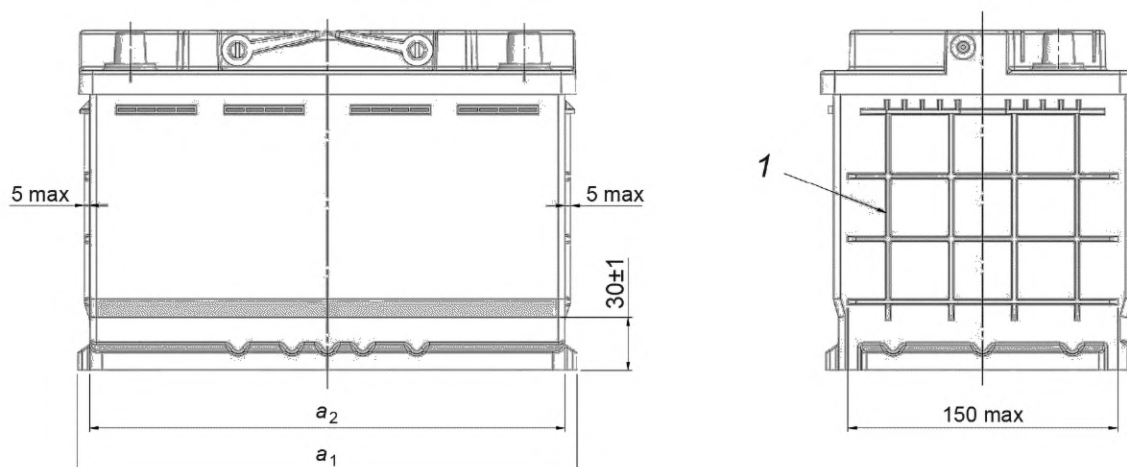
Размеры допустимого утолщения боковых стенок корпуса на коротких сторонах батареи
